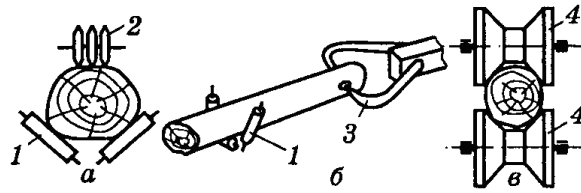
Базування заготівок циліндричної форми: *а* – колодопиляльного верстата; *б* – пилорами; *в* – корувального верстата; 1 – ролики; 2 – притискні диски; 3 – кліщі; 4 – подавальний валець
